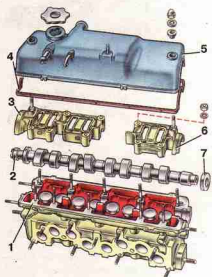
Разборка головки цилиндров: 1 – головка цилиндров; 2 – распределительный вал; 3 – задний корпус подшипников распределительного вала; 4 – прокладка; 5 – крышка головки цилиндров; 6 – передний корпус подшипников распределительного вала; 7 – сальник
